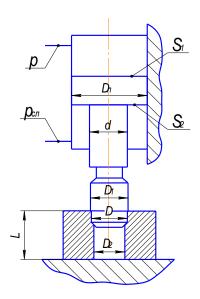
Схема сборки продольно-прессового соединения с натягом
